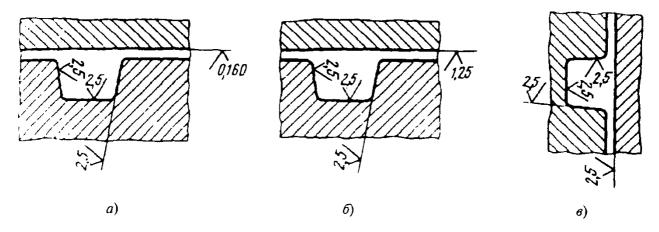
Шероховатость поверхности сопрягаемых деталей. Соединение: a - подвижное; δ - неподвижное; δ - торцовое
